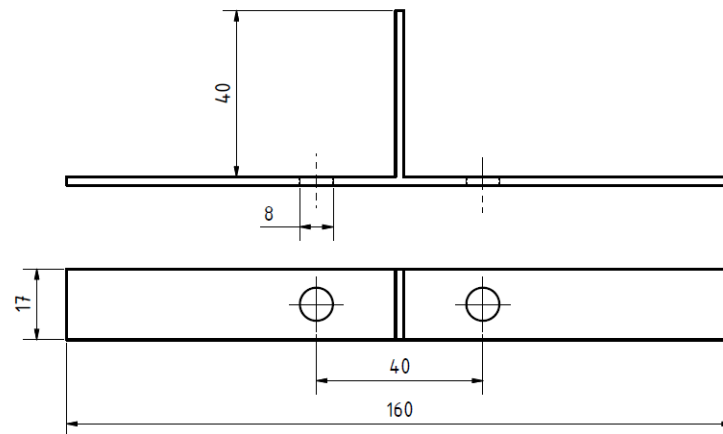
Geometria do provete para o ensaio de arrancamento (dimensões em mm)
